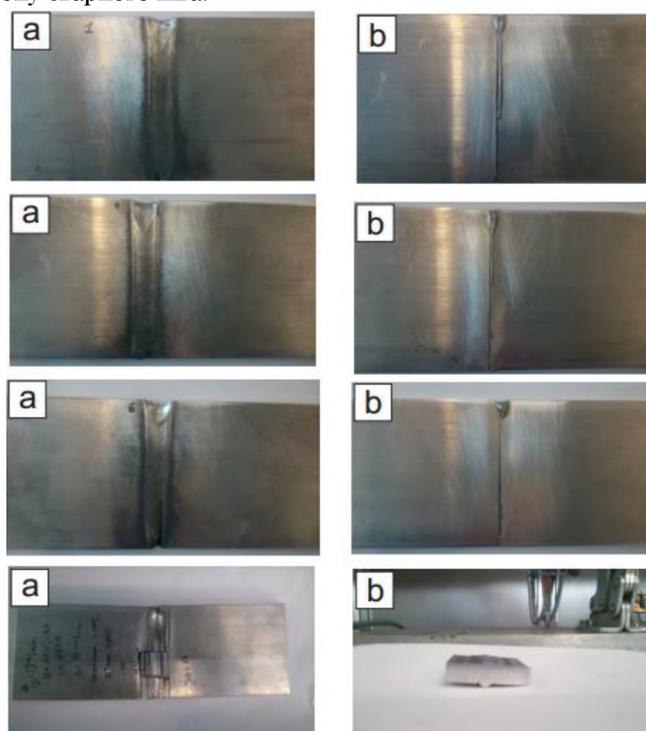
Сварные швы на сплаве AlSi1MgMn6082Т6:а)лицевая сторона;б)оборотная сторона
